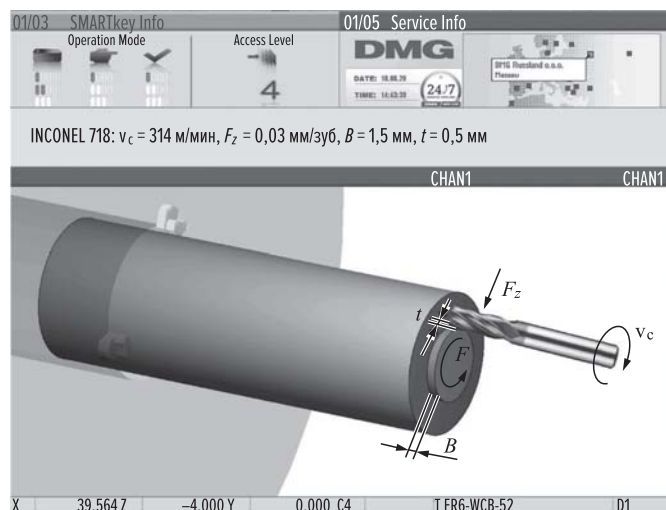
Стратегия испытаний и режимы резания при обработке концевыми керамическими фрезами заготовок из сплава INCONEL 718
